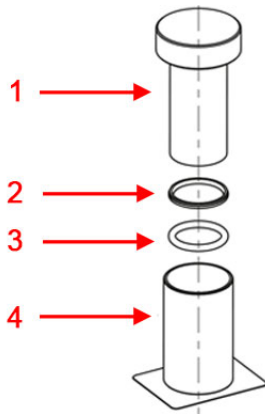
O-Ring in das Montagewerkzeug einsetzen
